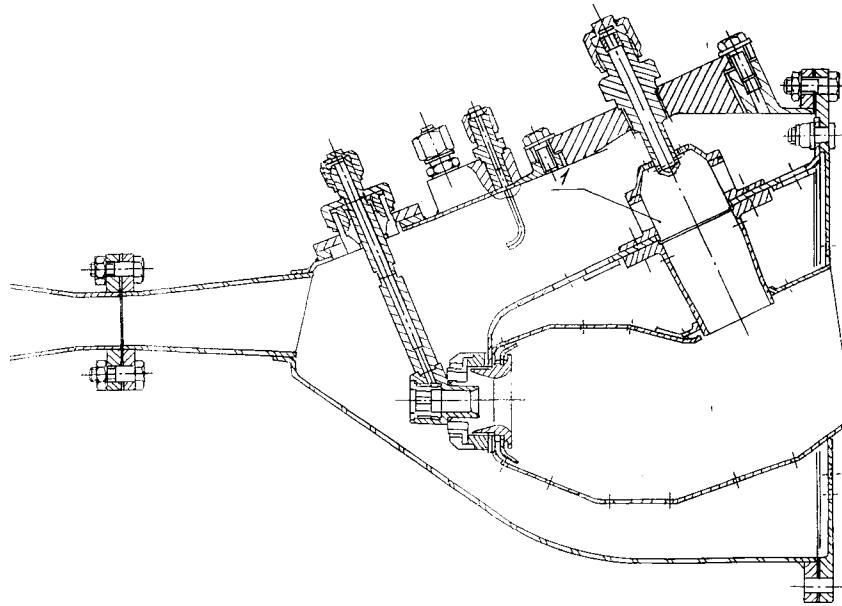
Схема приспособления для продувки горелок (1- испытываемая горелка)
